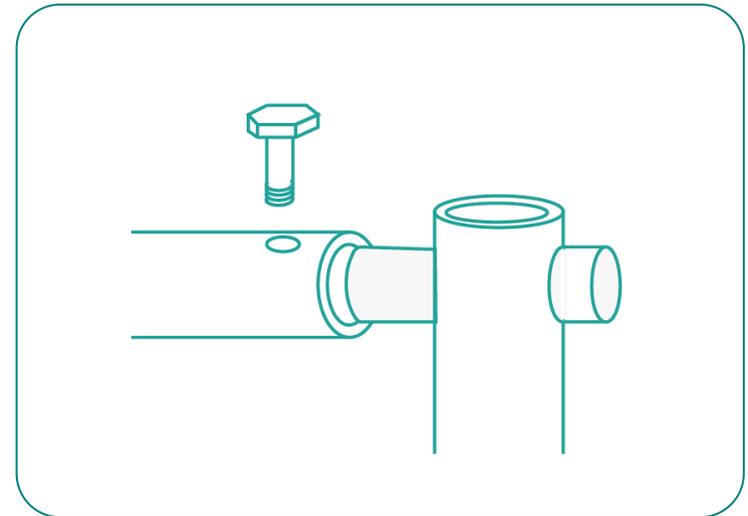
Ensamble , unión de columna travesaño, Elaboración propia
